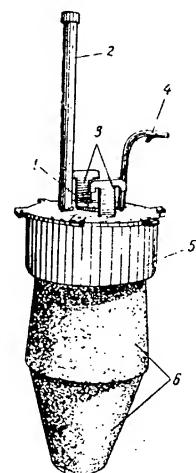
Общий вид огнеупорной камеры горения с закрепленной металлической крышкой:
